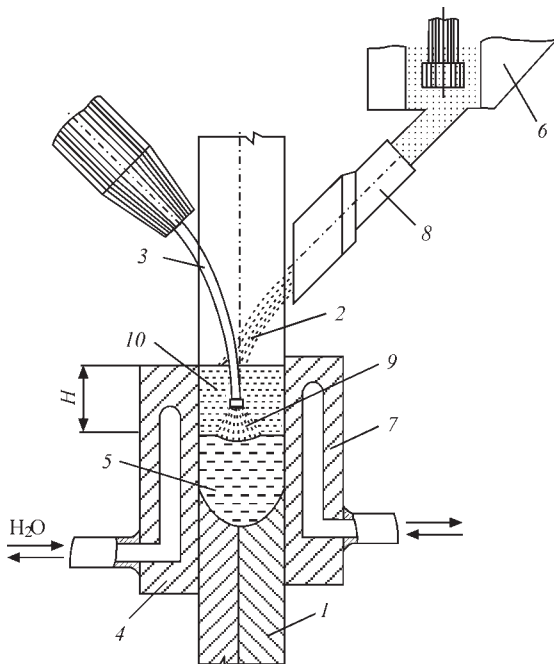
Схема методу зварювання з примусовим формуванням вертикальних швів під тонким шаром розплавленого шлаку дротами суцільного перерізу: 1 – зварний шов; 2 – флюс; 3 – електродні дроти; 4 – передній повзун; 5 – зварювальна ванна; 6 – флюсобункер; 7 – задній формуючий повзун; 8 – мідне сопло; 9 – зварювальна дуга; 10 – рідкий шлак
